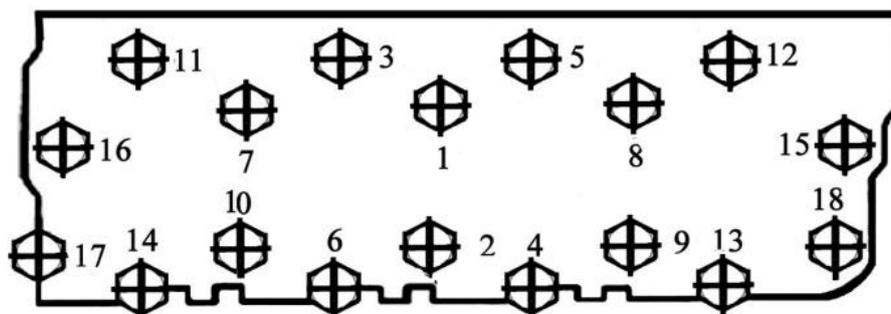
Порядок затяжки болтов (гае-) крепления головки блока цилиндров двигателя ЗМЗ-66-06
